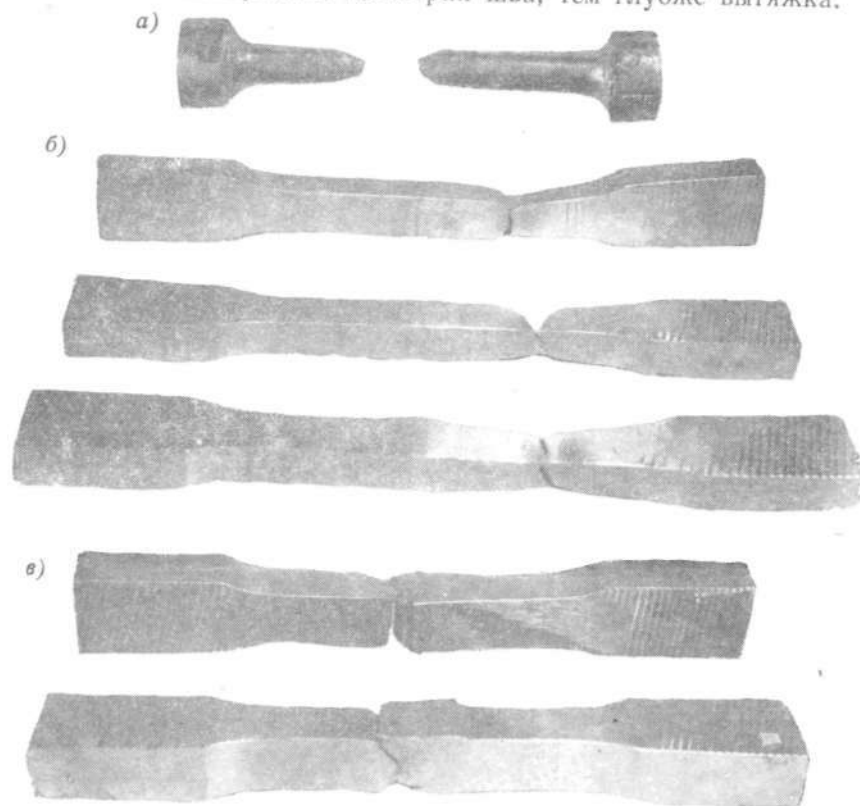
Образцы, подвергшиеся растяжению: а — при испытании металла шва; снятие усиления; б — при испытании тонкостенных
